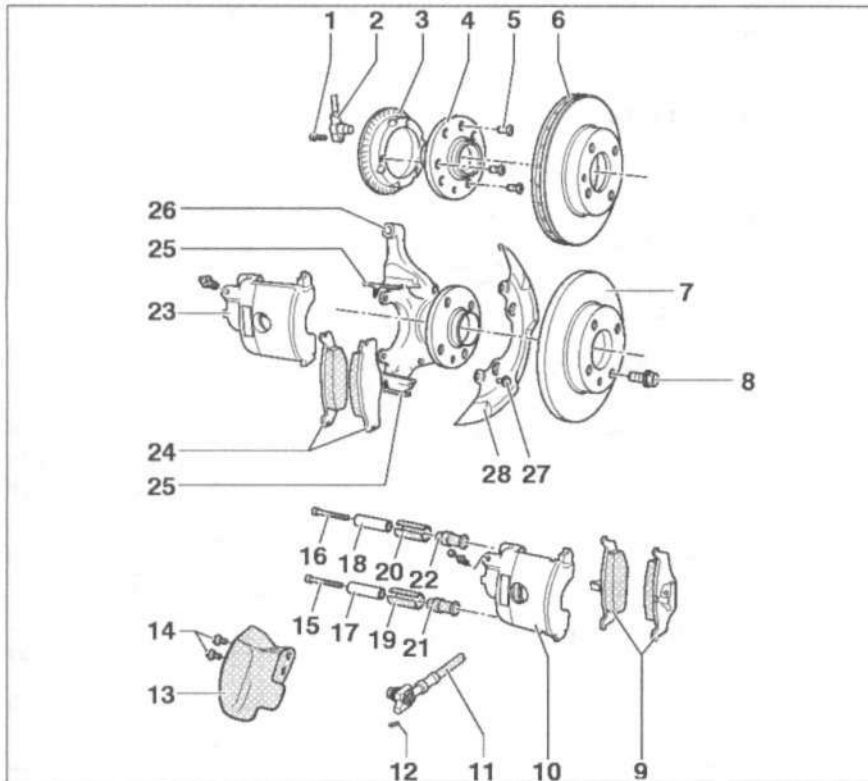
Передние тормозные механизмы с тормозными суппортами VW I и VW II:
